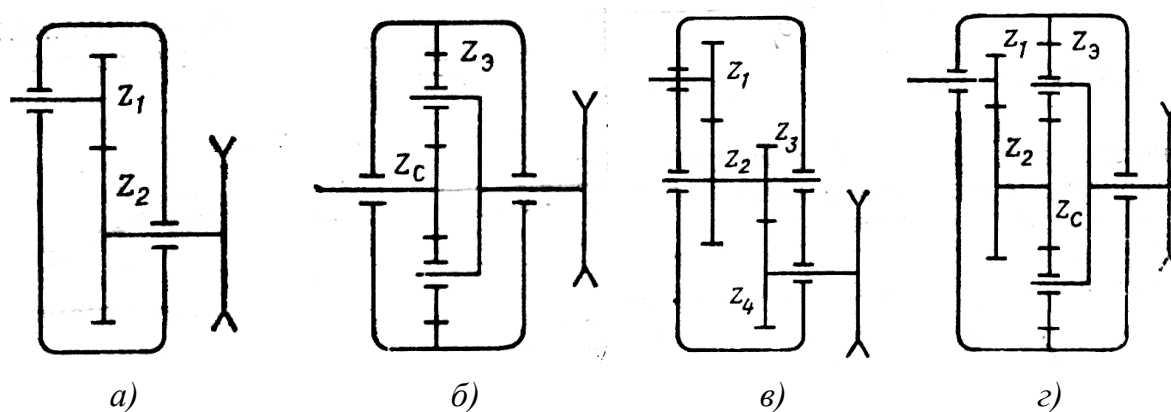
Схемы бортовых редукторов: а, б – однорядные; в, г – двухрядные
